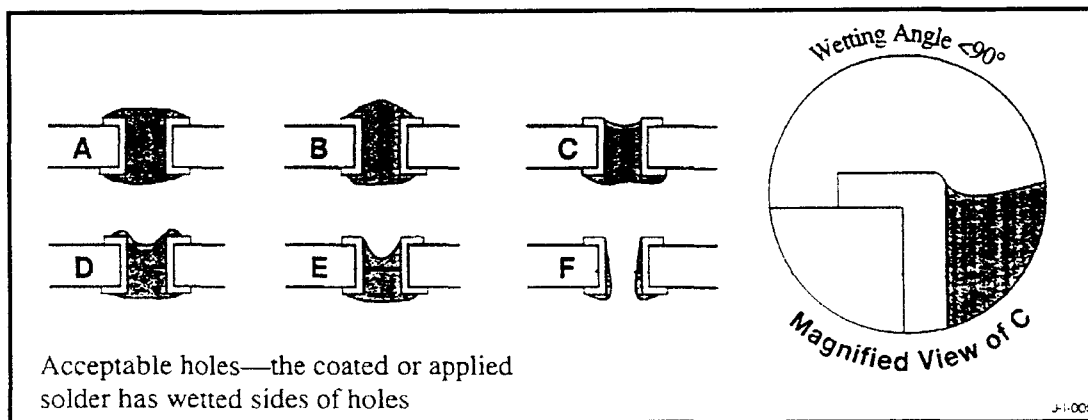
1 Soldadura en el *plated through-hole* sin terminales [1]
